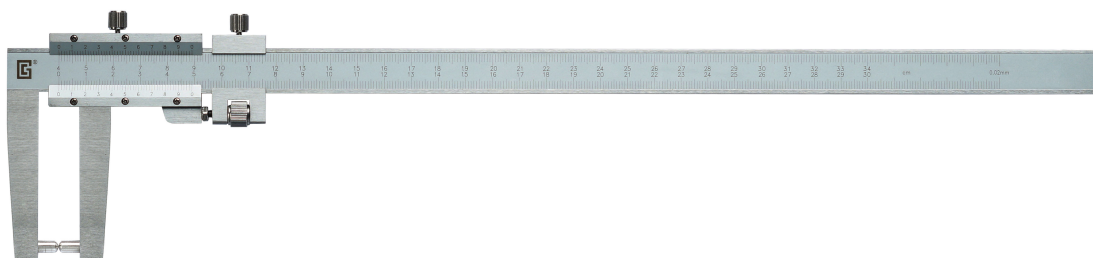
Общий вид штангенциркулей модели ШЦС-116, тип В
